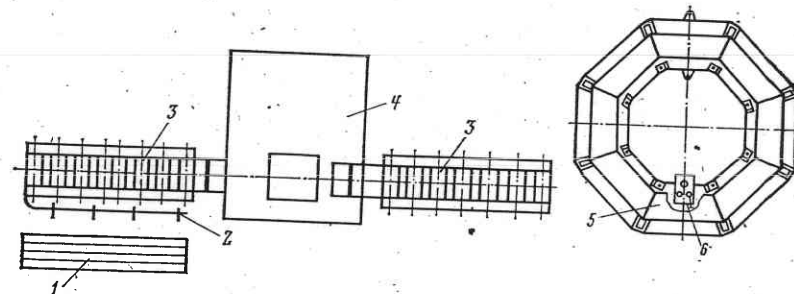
Поточная линия для изготовления спиральных армокаркасов: 1 — загрузочное устройство; 2 — сбрасыватель; 3 — подающее устройство; 4 — цех стыковосварки; 5 — навивочное устройство; 6 — гибочно-протяжной механизм
